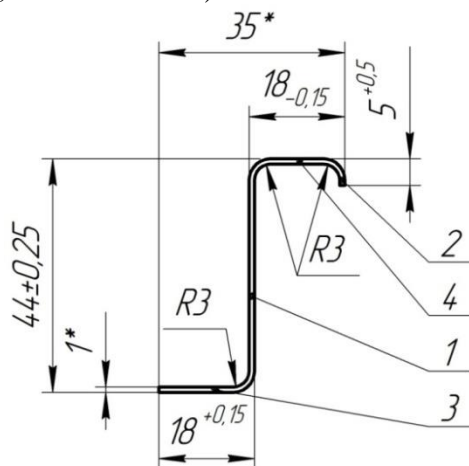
Поперечное сечение Z-образного профиля для заготовки шпангоута
